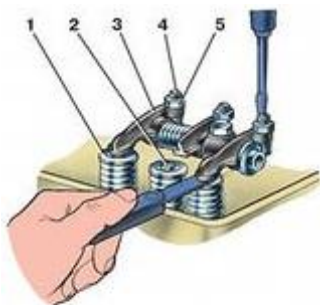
1- тарелка пружины, 2 - шпindelь клапана, 3 - коромысло, 4 - регулировочный винт, 5 - контргайка
